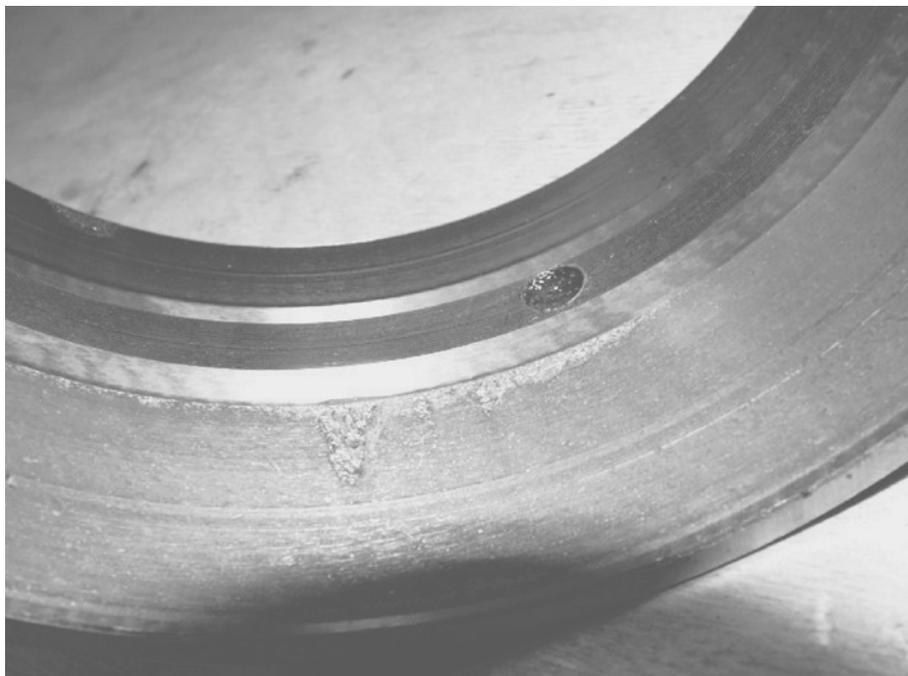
Абразивный износ рабочей поверхности кольца подшипника
